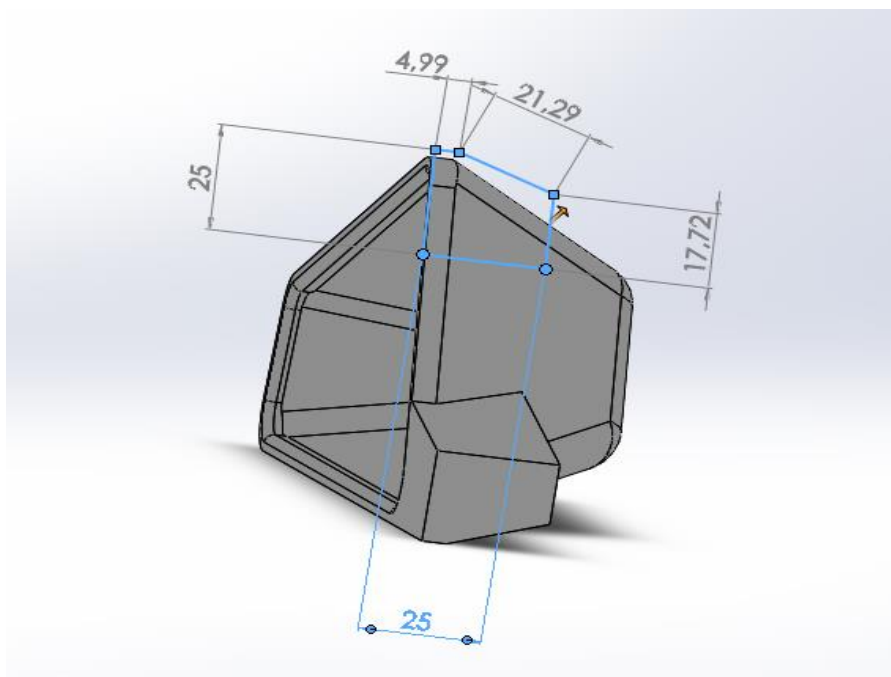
Definición general de las dimensiones de forma para la construcción del anclaje superior del retrovisor B.
